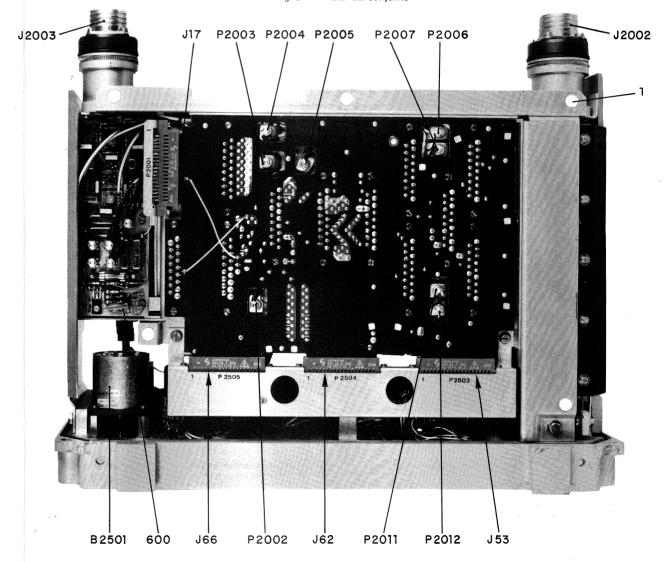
Vue de dessous Fig.4 Underside view Fig. 4 Vista de debajo
